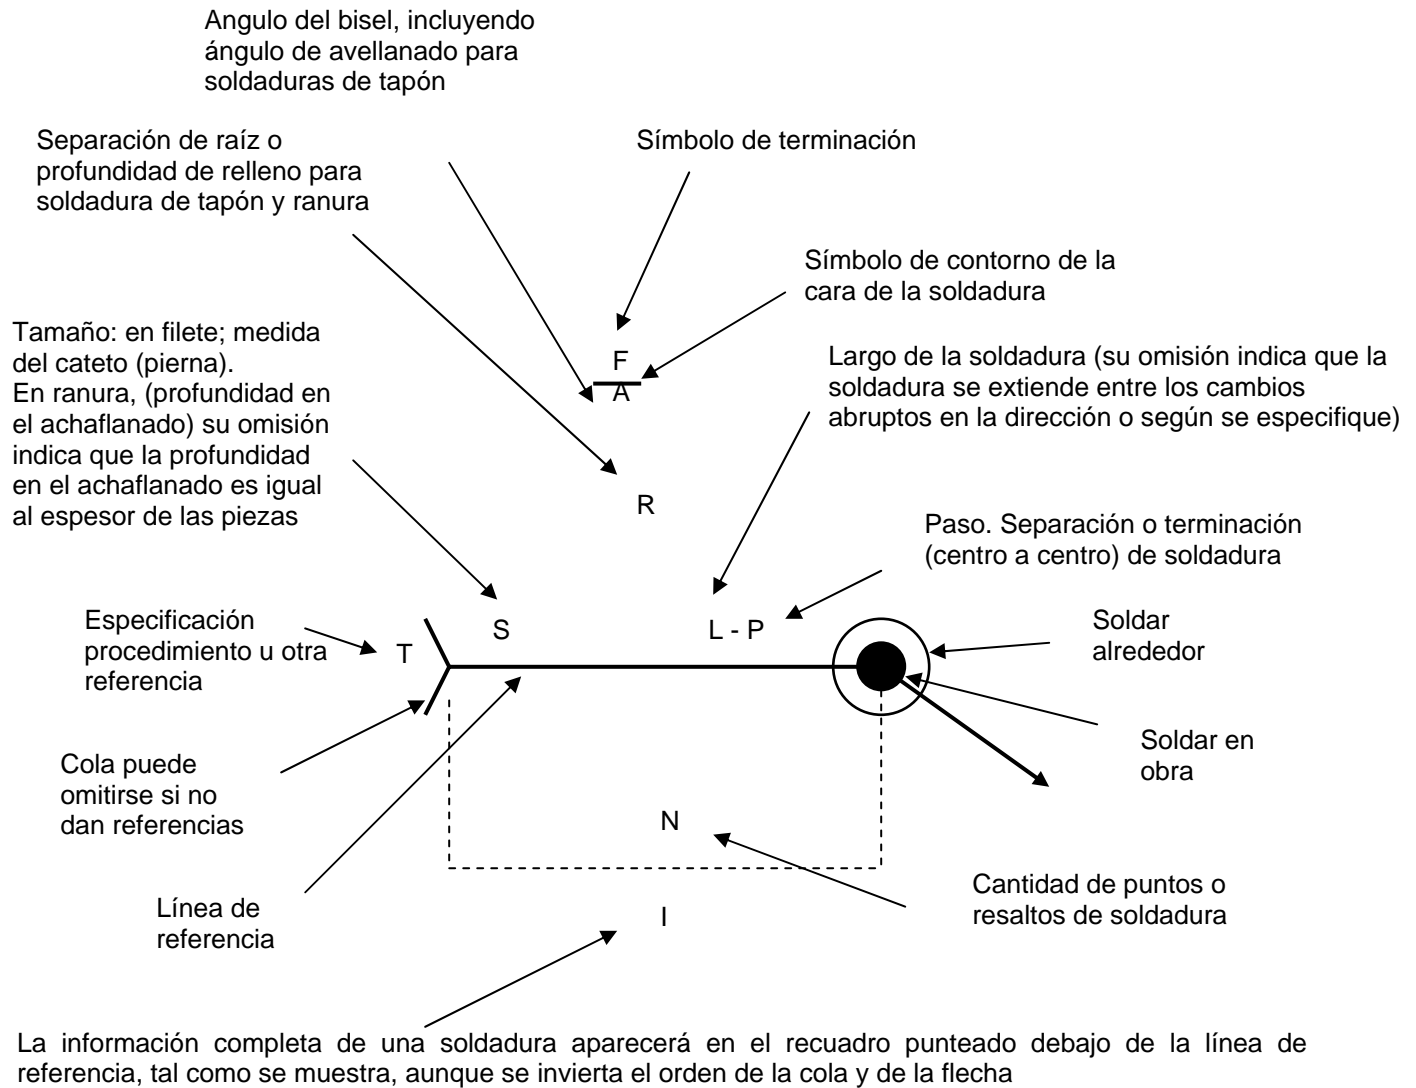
Simbología de soldadura que se utiliza en planos
